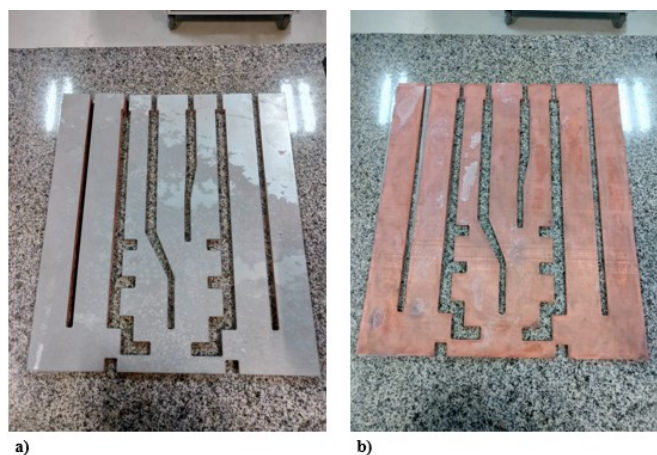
a) Chapa cortada junto das malhas para facilitar o corte. b) Malhas cortadas na geometria de projeto.
